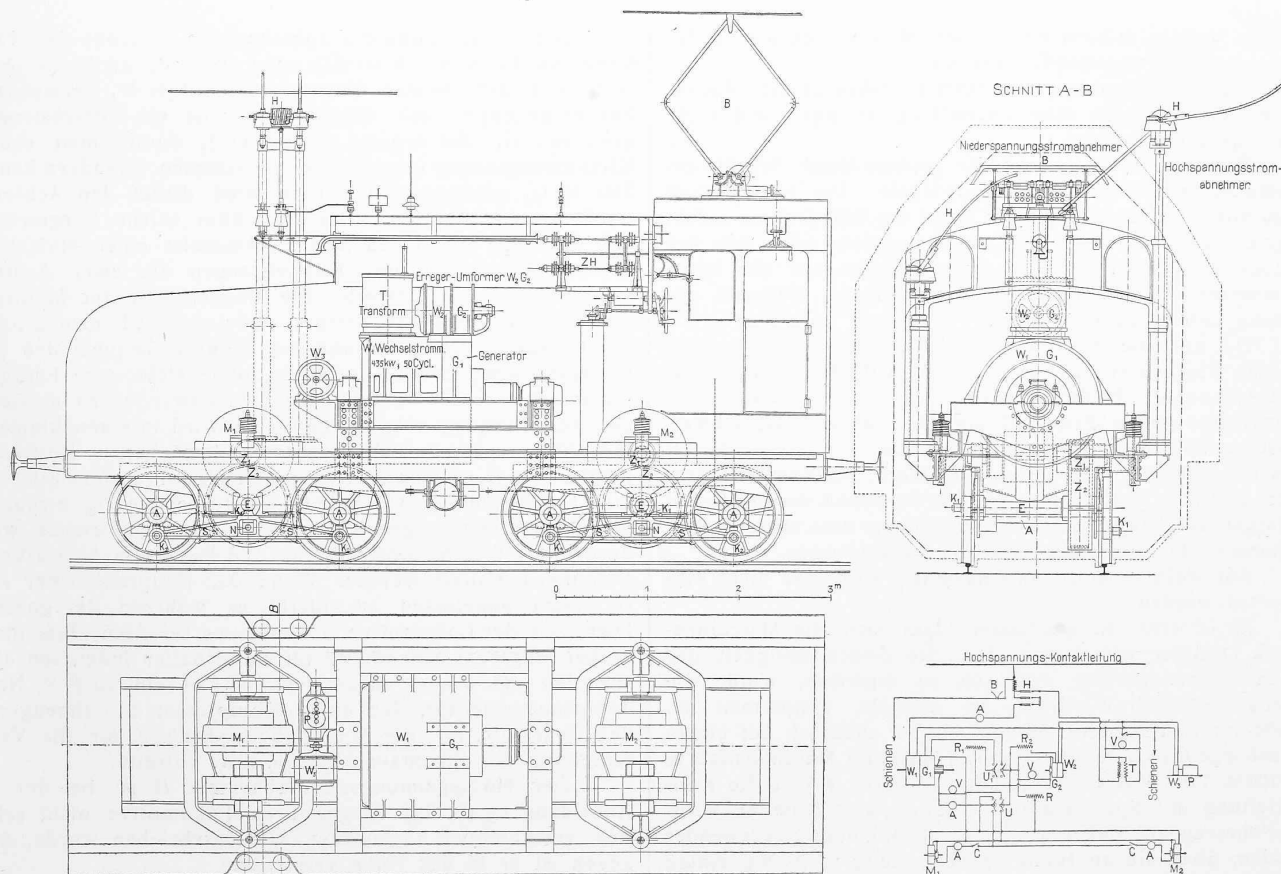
Umformerlokomotive. — Ansicht, Grundriss und Schnitt. — Masstab 1:75. — Schaltungsschema.
